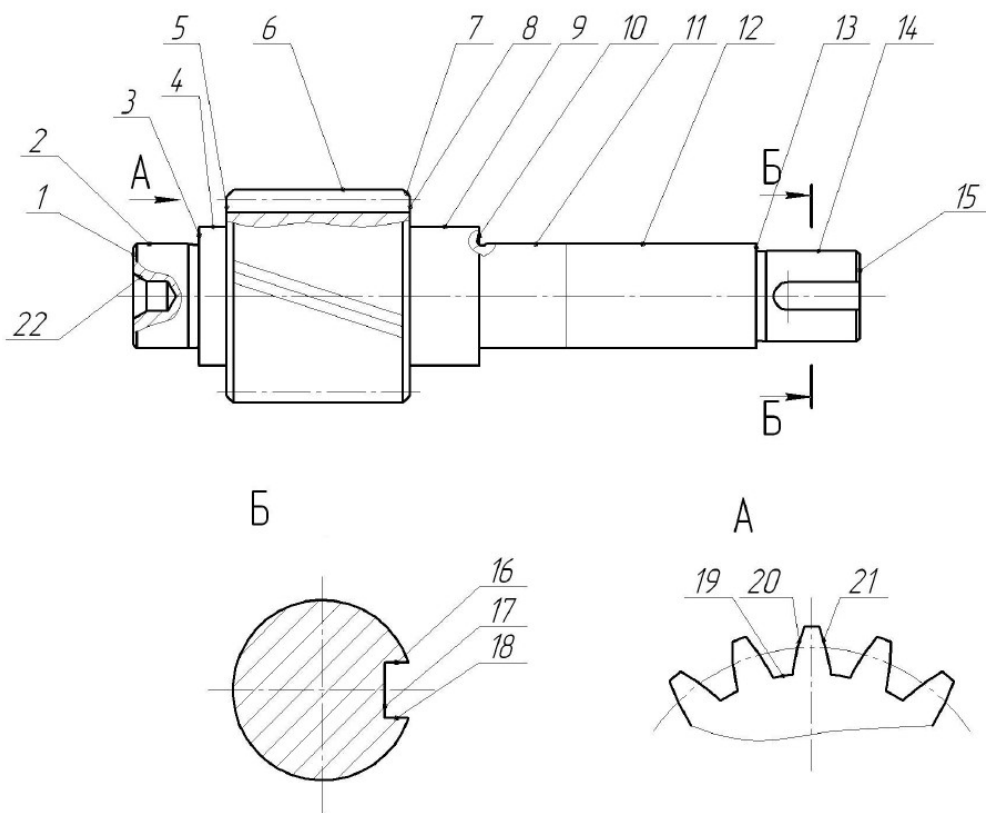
Вал-шестерня редуктора SZ 121
